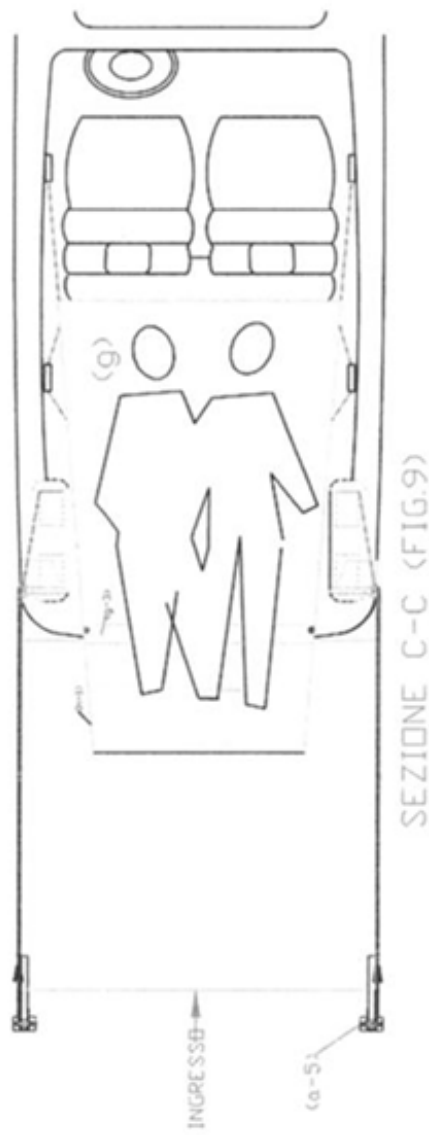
VISTE IN PIANTA AUTO CON TENDA A CASSETTA
